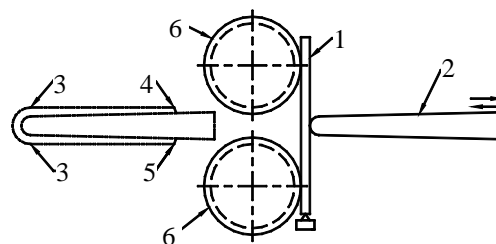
Схема прокатки или вытяжки с изгибом заготовки
